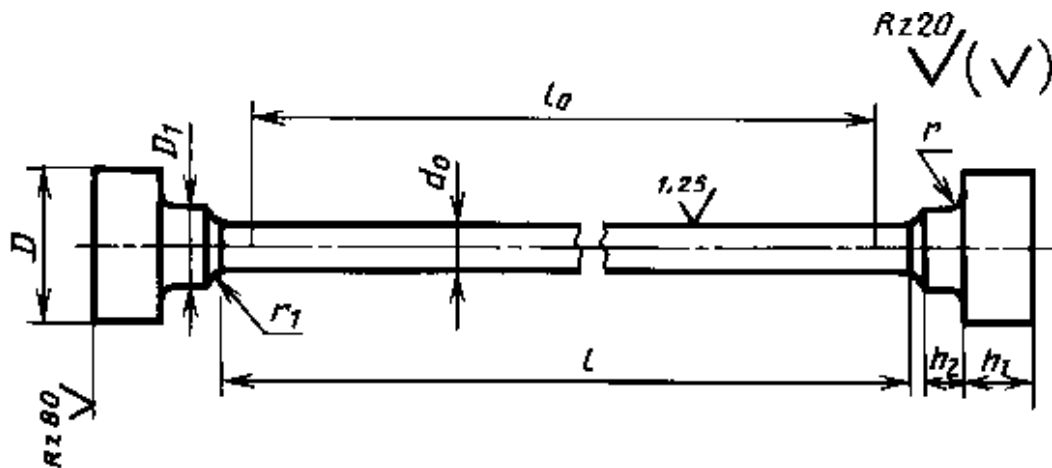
Механічно оброблений зразок за ДЕСТ 1497-84
